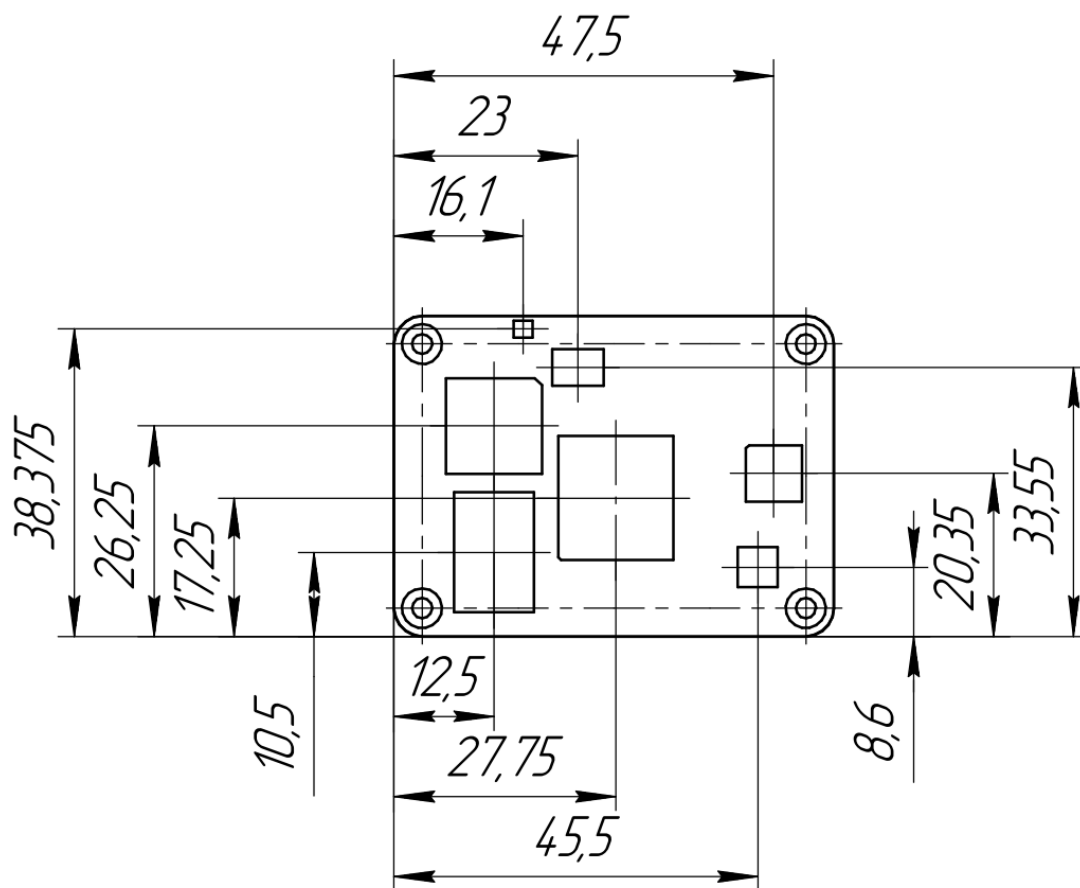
Чертеж ELTAY RM66, вид сверху.
